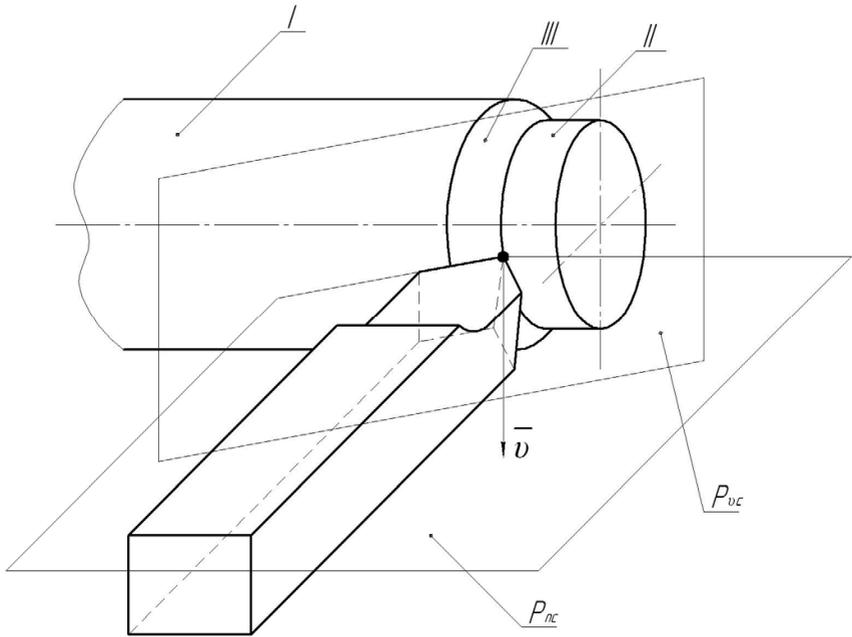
Координатные плоскости в статической системе координат: I – обрабатываемая поверхность заготовки; II – обработанная поверхность заготовки; III – поверхность резания;  $P_{yc}$  – плоскость резания;  $P_{nc}$  – основная плоскость
